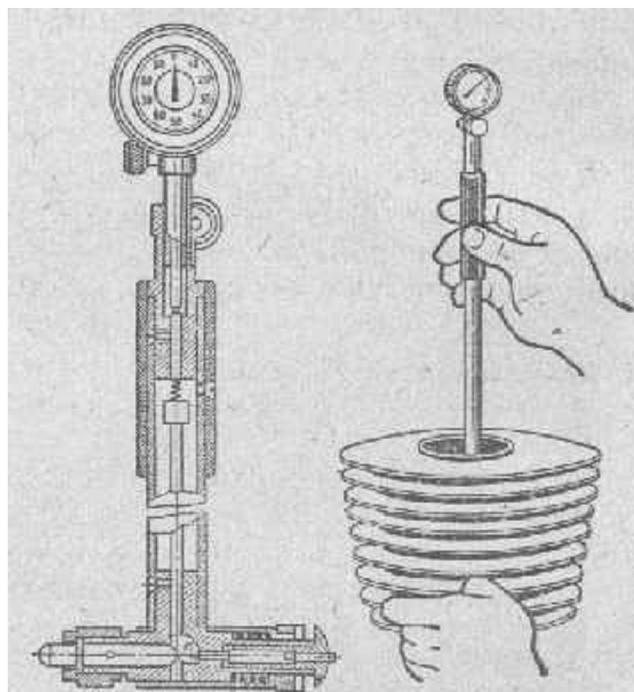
Индикаторный нутромер и измерение им диаметра цилиндра
